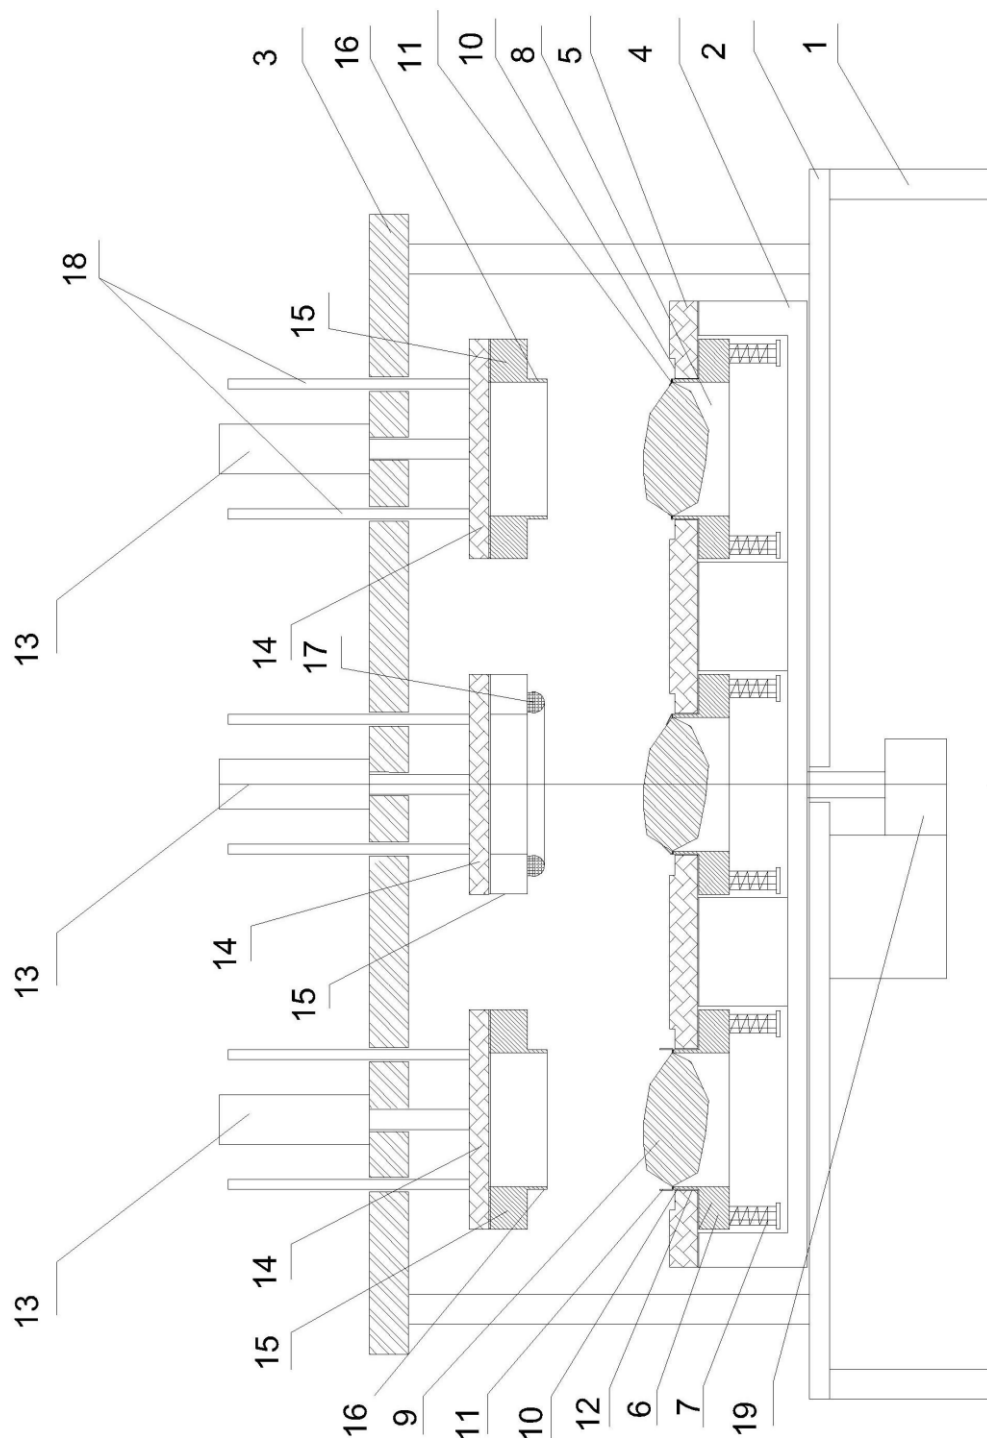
Общий вид станка для упаковки изделий в отформованной фольге с поднятыми вверх прижимами после осуществления формовки на каждой стадии формовки
